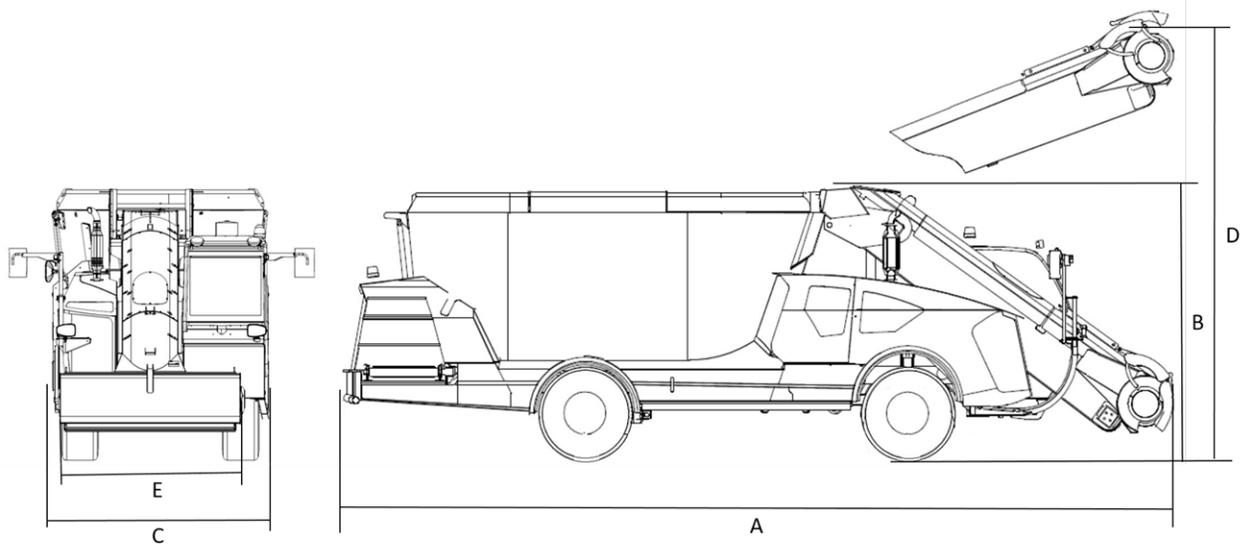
Dimensions — Mélangeur SMARTMIX automoteur
